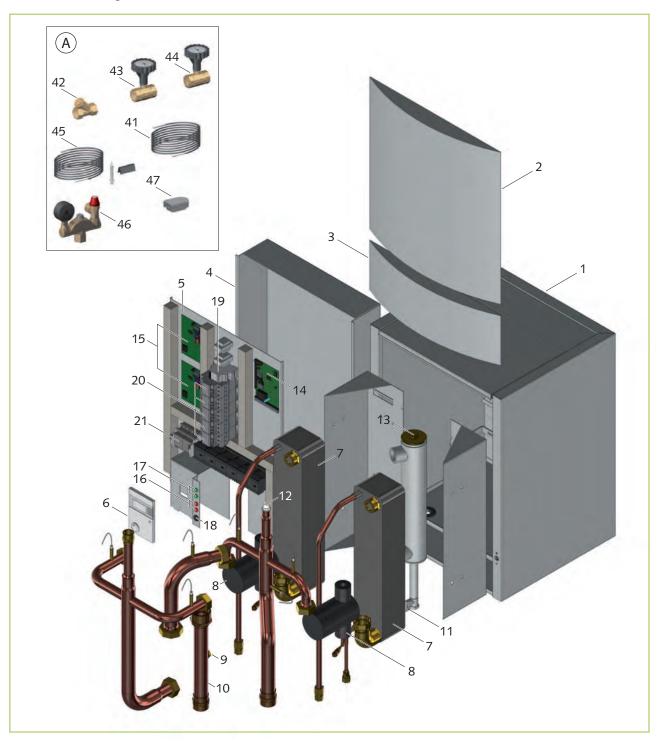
Explosionszeichnung Innenmodul CMF 180 Duo
